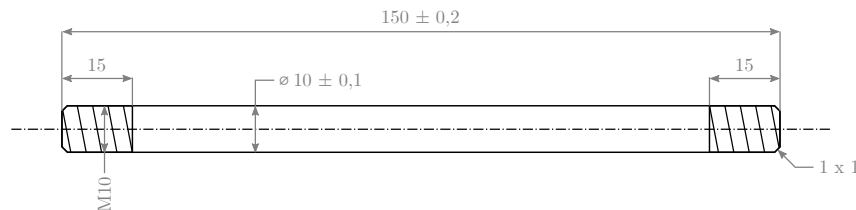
Géométrie d'éprouvette sans rétreint (dimensions : mm).
